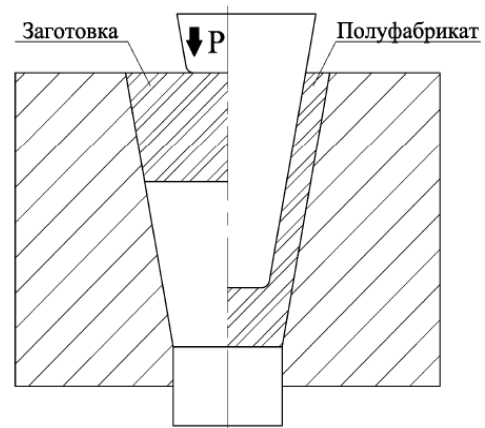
Исходная заготовка и схема процесса получения полой конической детали
